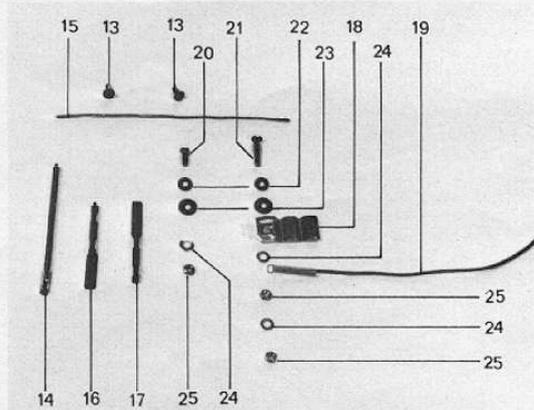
Bauteile der Gleisanschlüsse 7—9 und 11—13
